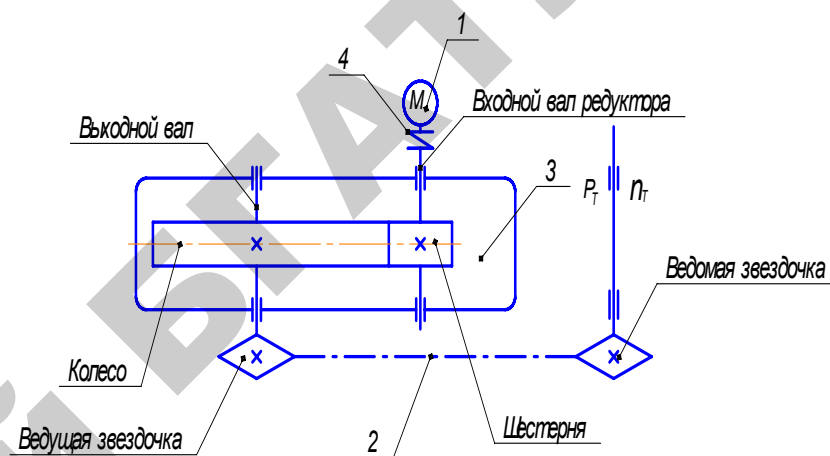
Кинематическая схема привода с цилиндрическим одноступенчатым редуктором и цепной передачей
